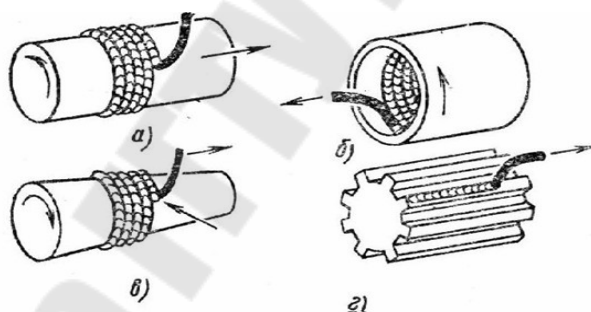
Схемы вибродуговой наплавки изделий различной формы:
